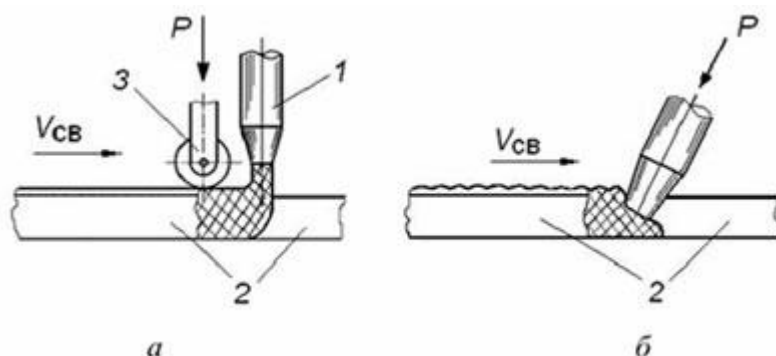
Схема безконтактної (а) і контактно-екструзійної (б) зварки розплавленим матеріалом:
